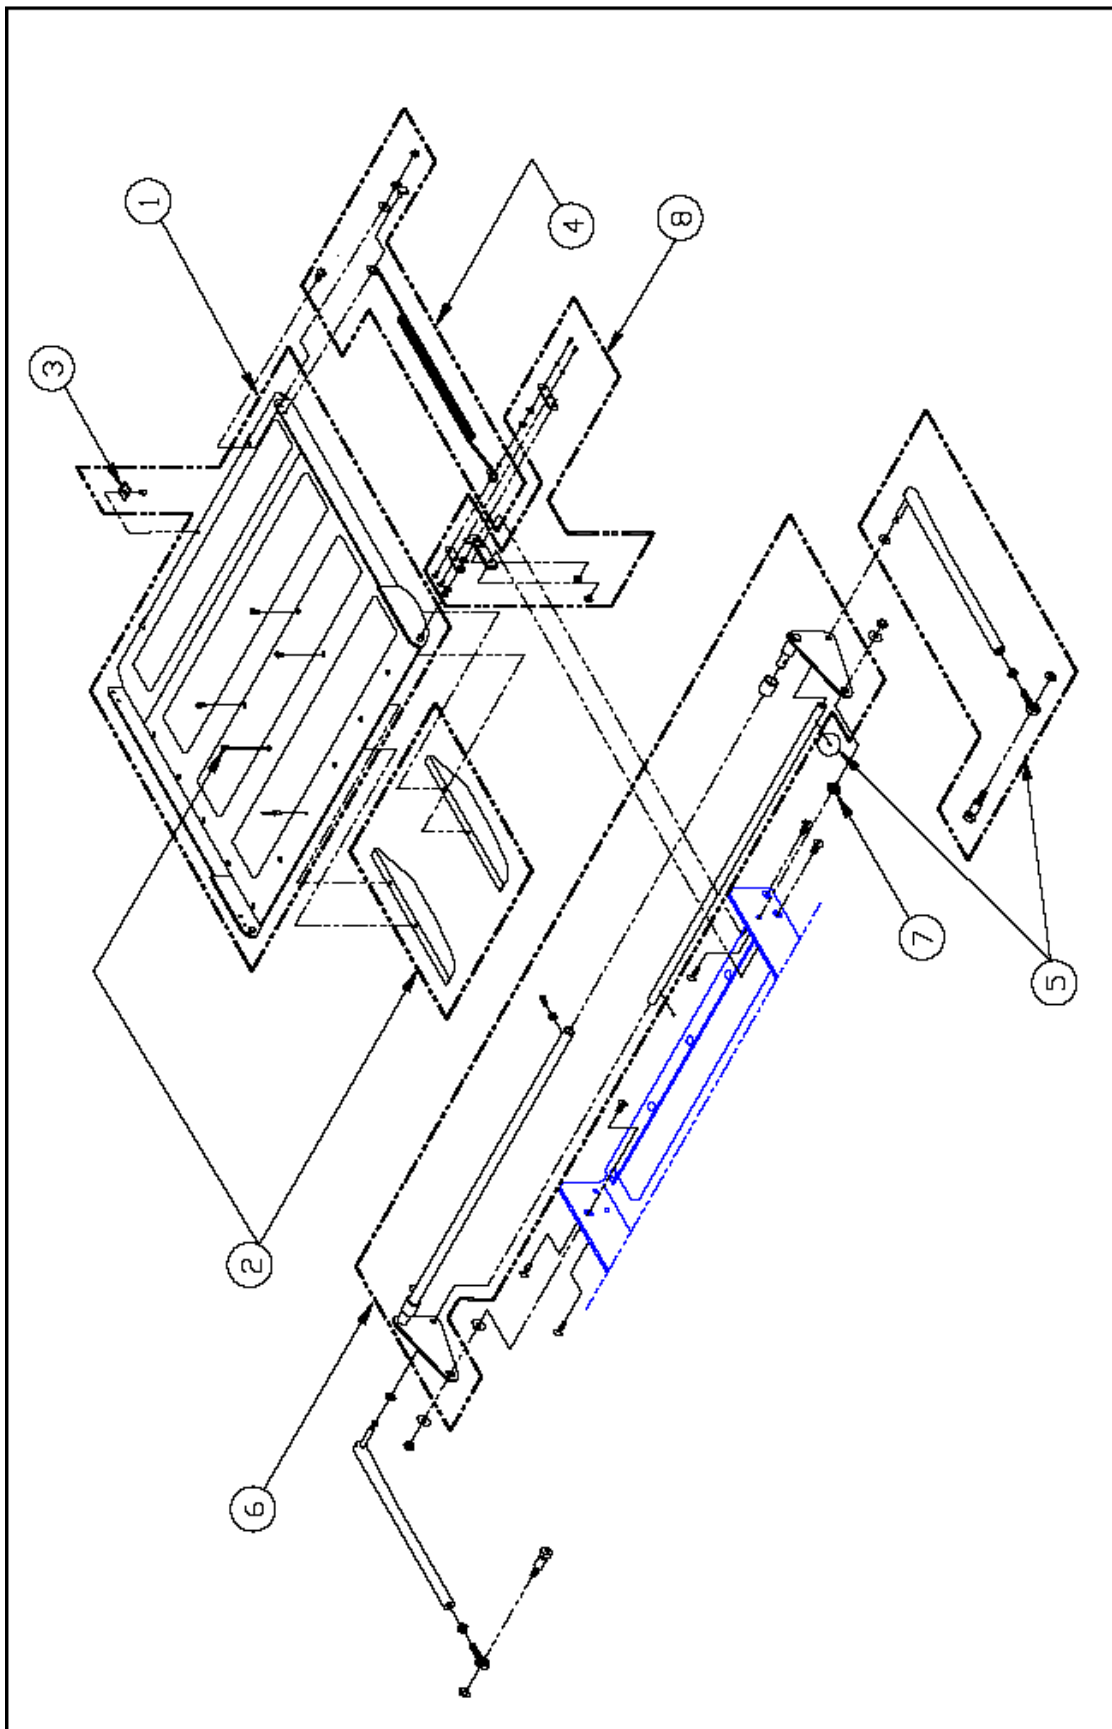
SPONDA DI COLLEGAMENTO F9T – CON GRADINI
